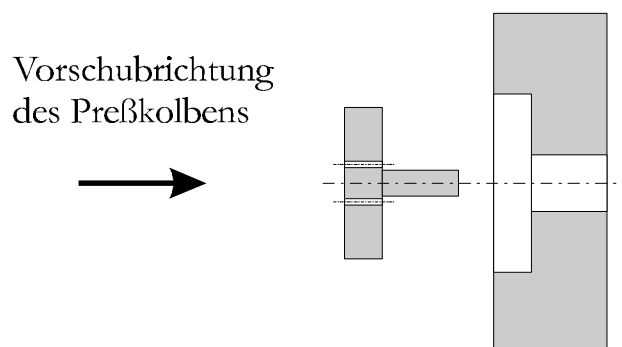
Explosionszeichnung des Mundstückes für die Herstellung von Hohlzylindern.
